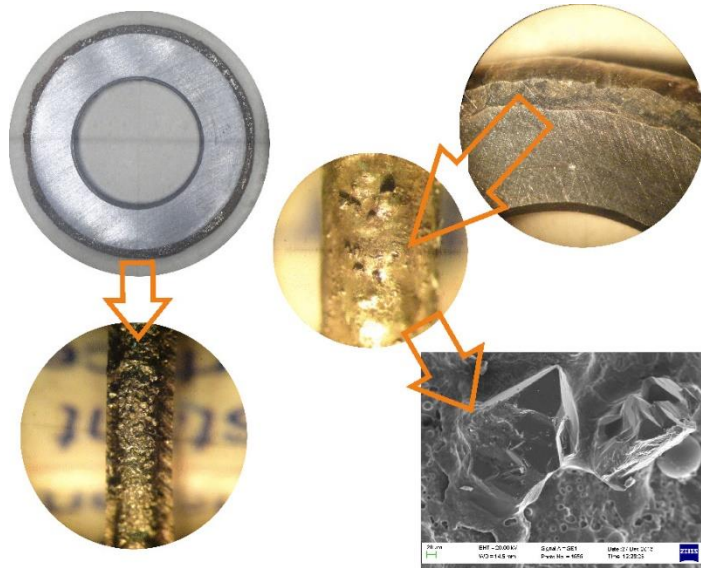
Формування абразивного шару за допомогою попереднього наплавлення на циліндричній поверхні
